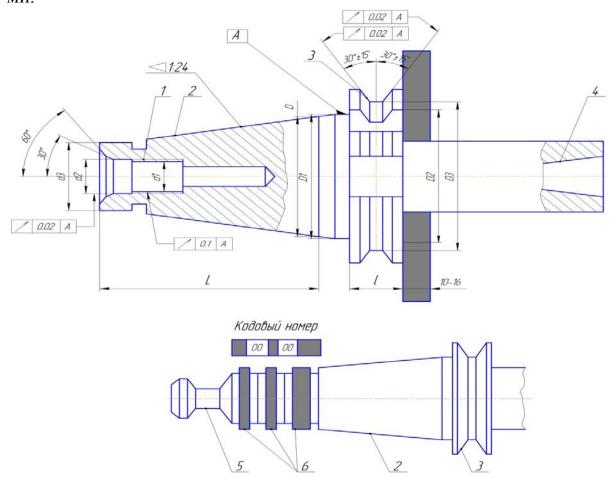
Базовые оправки для станков с ЧПУ с системой АСИ
